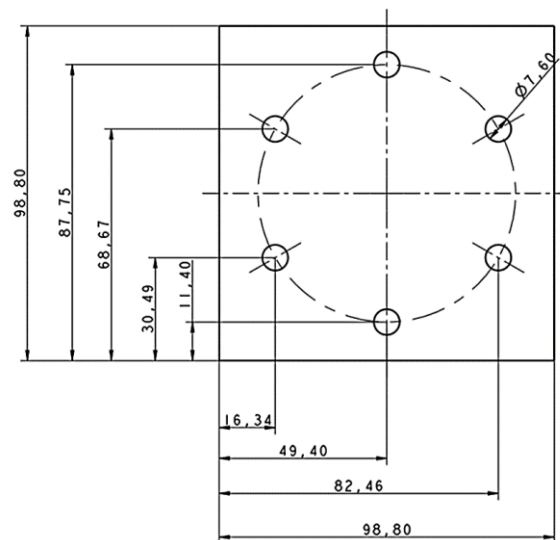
Technische Zeichnung der Rohlinge für die idealen Leckagen (Maße in mm).
